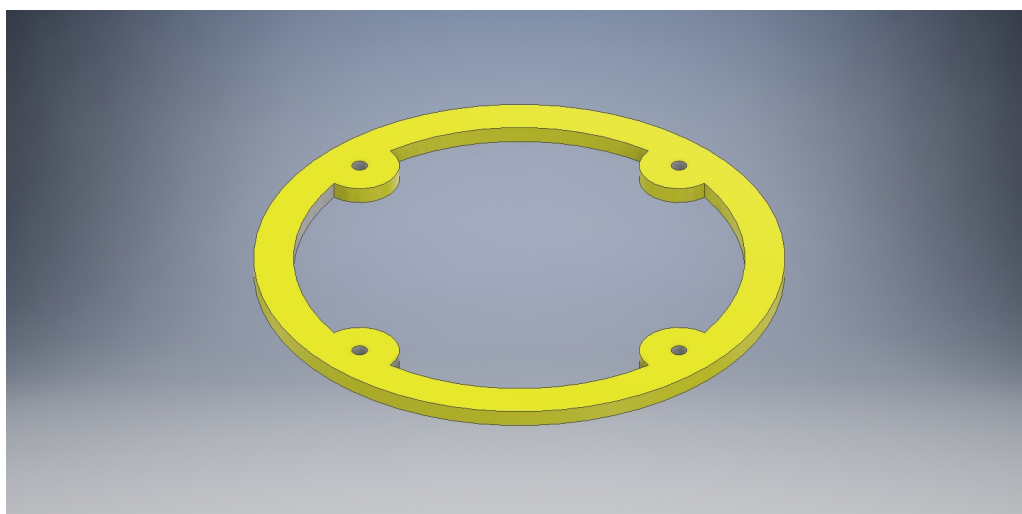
Parte intermedia del diseño mecánico del dispositivo esclavo
